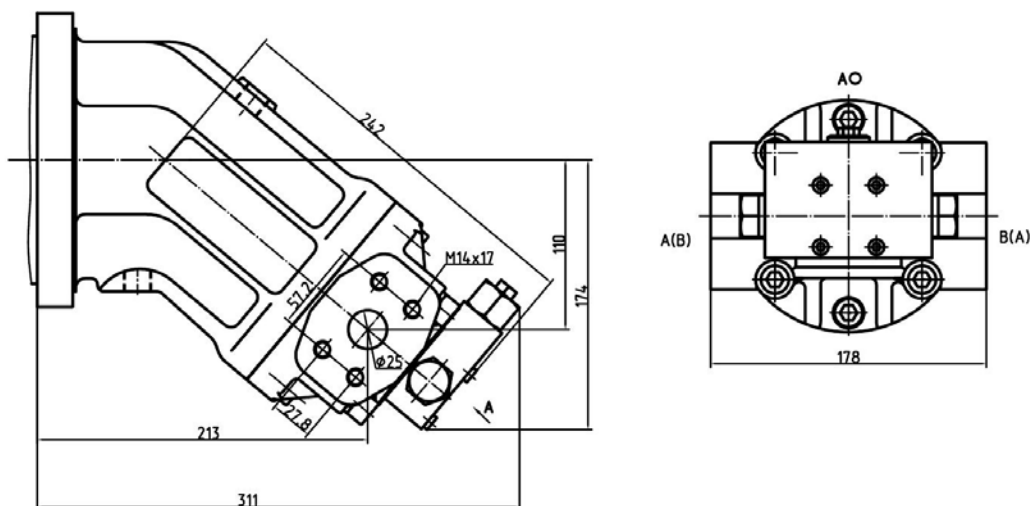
Габаритные, присоединительные размеры в гидромоторах 410.0.107(125).
